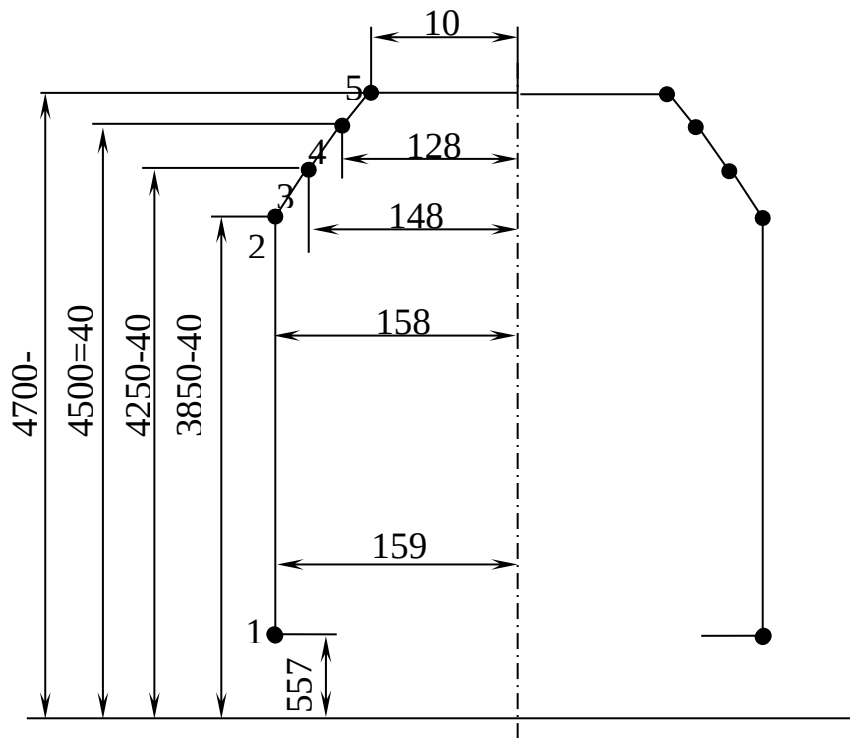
Вертикальний габаритний каркас конструкції контуру кузова вагону.
